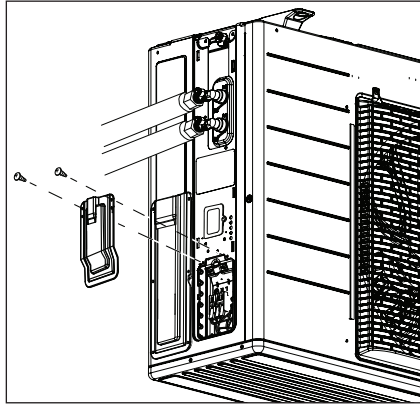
Retirer le deuxième couvercle pour accéder à la carte électrique.
